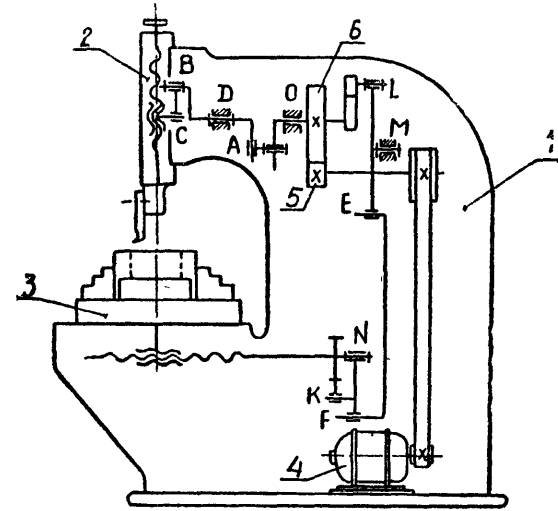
1. Общий вид долбежного станка с вращающейся кулисой
